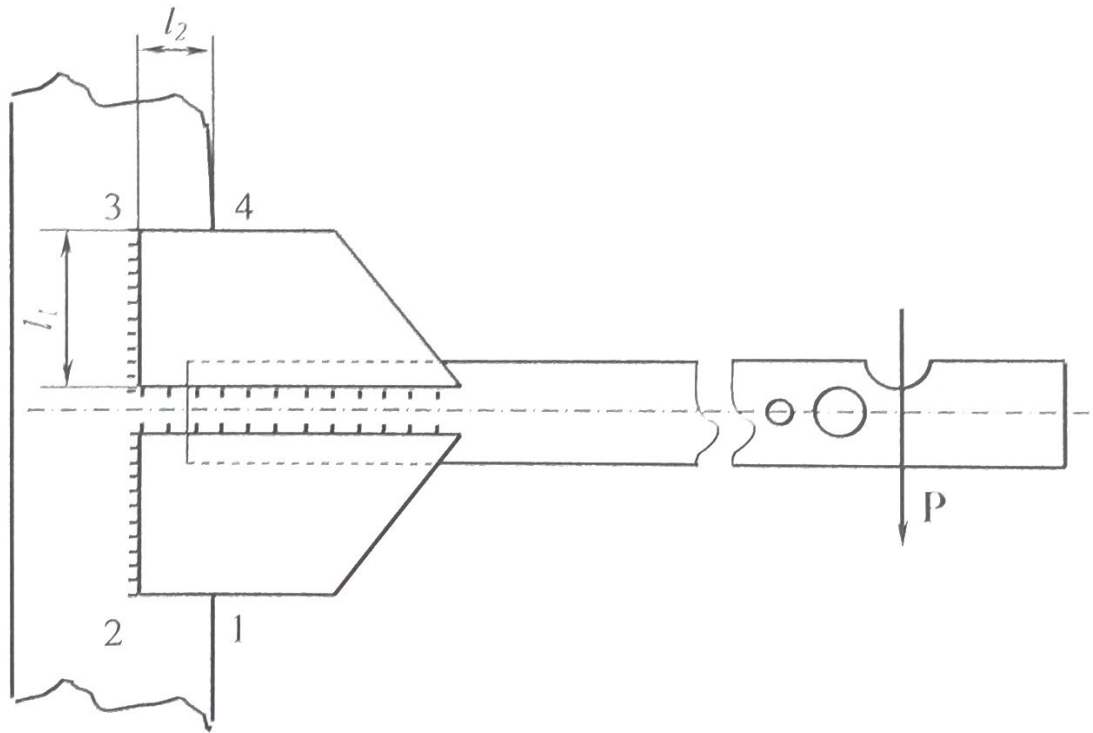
Схема зварного з'єднання тяги і стійки пристосування
